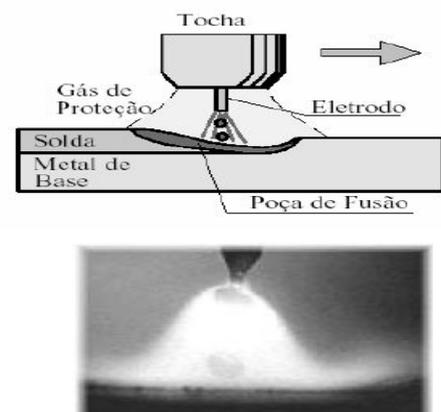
Resumo de soldadura MIG/MAG. Fonte - Altino Loureiro
